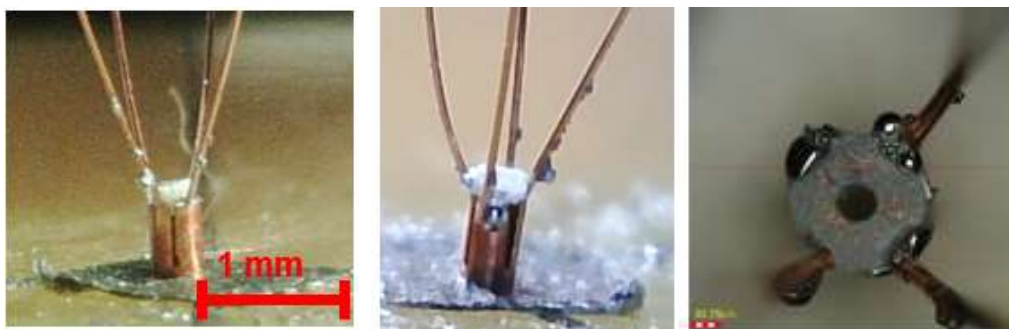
Cables soldados al estátor del microactuador 1Fr.
